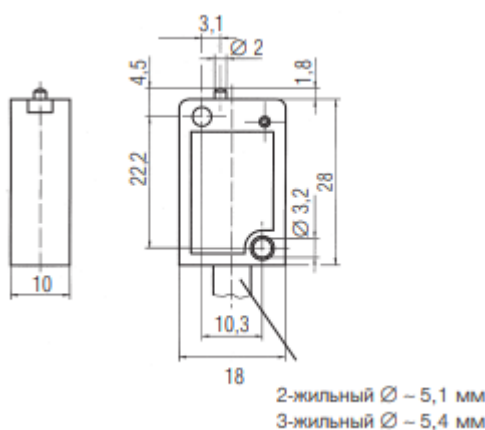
Габаритные и присоединительные размеры концевого выключателя
